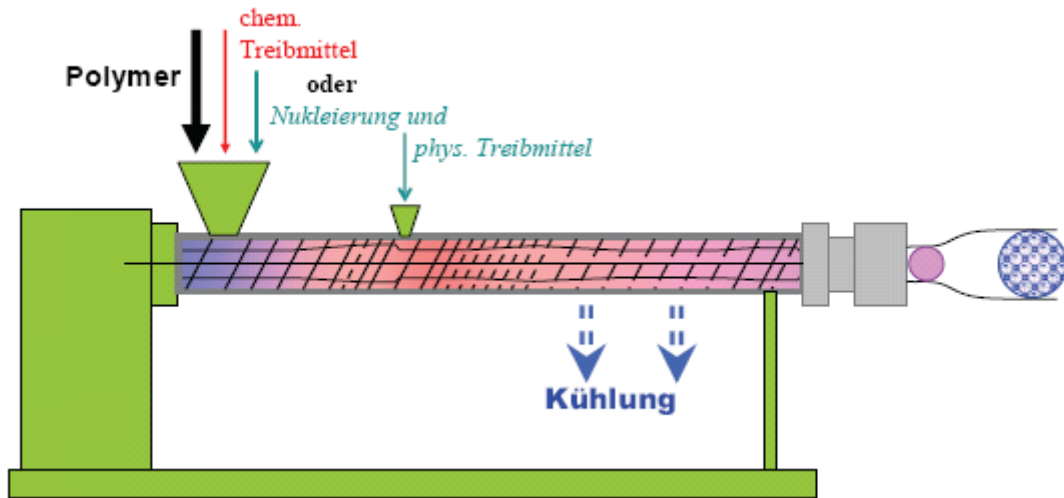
Prinzipskizze zum Extrusionsschäumen [32]
